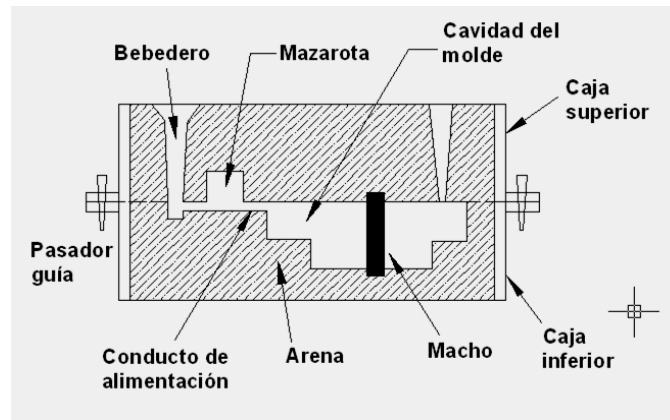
ESQUEMA DE MOLDE LISTO PARA SER LLENADO.
